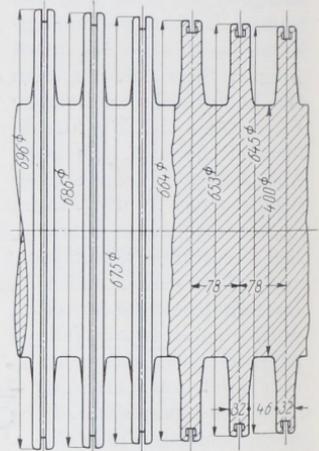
Mit der Welle aus einem Stück gedrehter Läufer, AEG, Berlin. M. 1:10.
